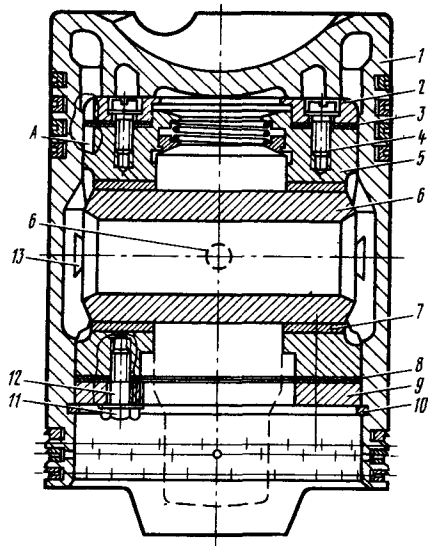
Поршень бесшпильчной конструкции (нижний):
